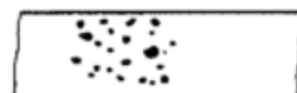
焊缝厚度  $3 < T \leq 6$  mm
